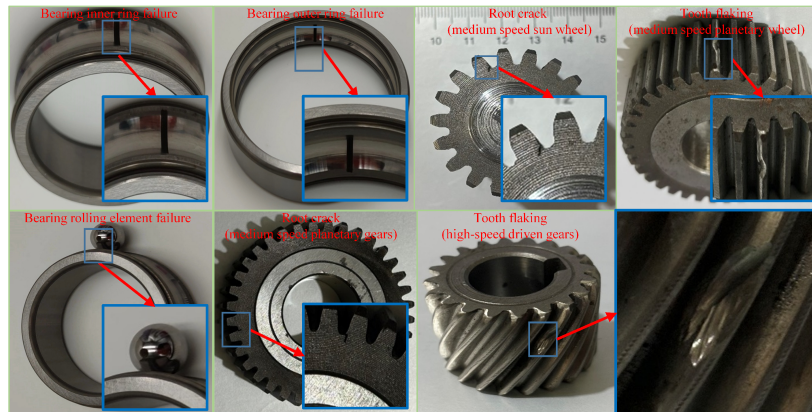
Défaut combiné d'engrenage et de roulement [44].
